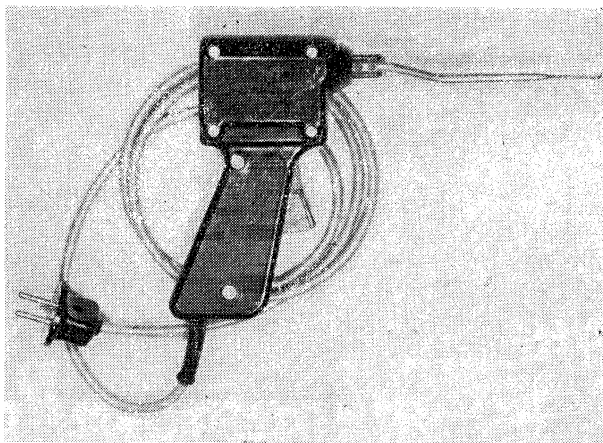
Moderne elektrische Lötpistole mit Beleuchtungslampe
